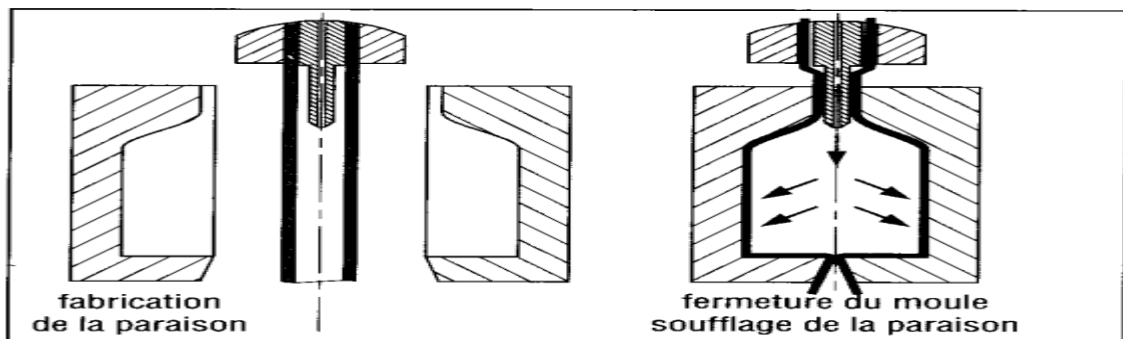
principe de fabrication d'une bouteille en extrusion-soufflage [2]
